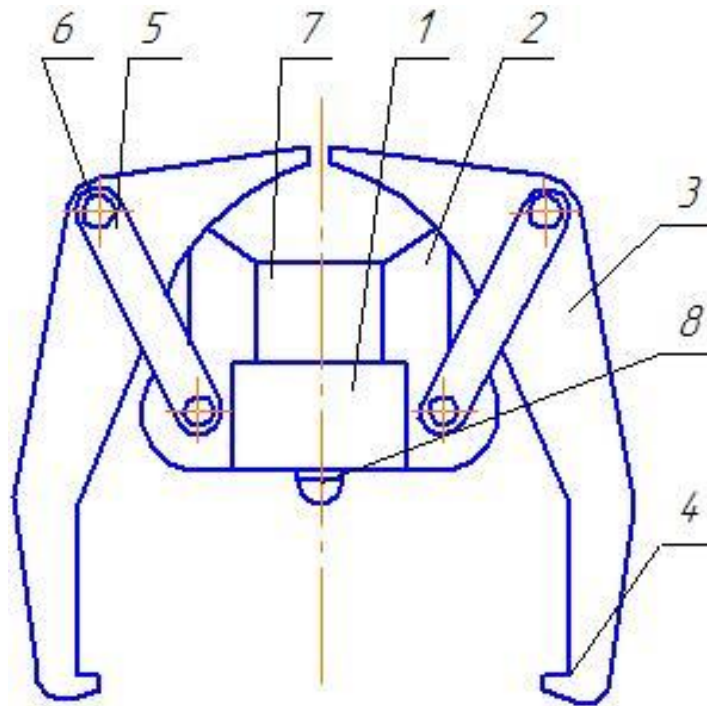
Гідравлічний знімач: 1 – поперечка; 2 – кронштейн; 3 – лапи; 4 – захоплююча частина; 5 – тяга; 6 – шарнір; 7 – гідроциліндр; 8 – опорна частина.
